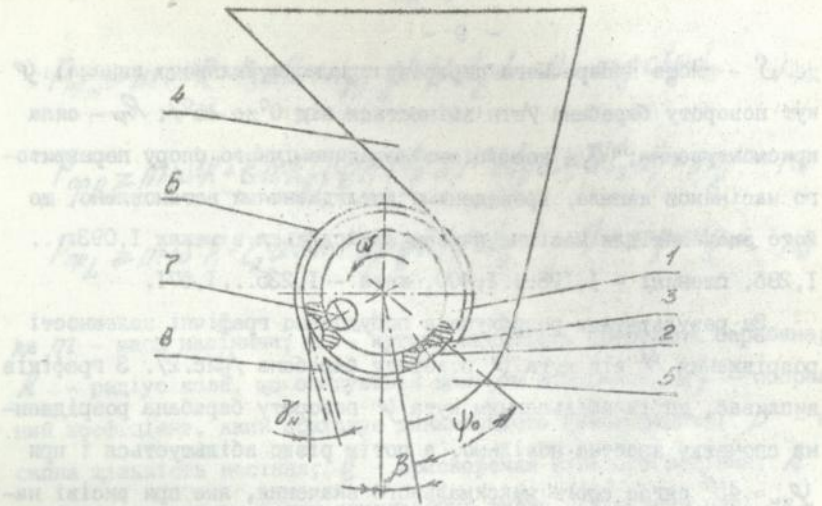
Схема пневматичного апарата барабанного типу для точного висіву: 1 - барабан; 2 - комірчина; 3 - канал; 4 - бункер; 5 - забірна камера; 6 - кожух; 7 - валець-відсікач; 8 - насінне-приймальний канал
